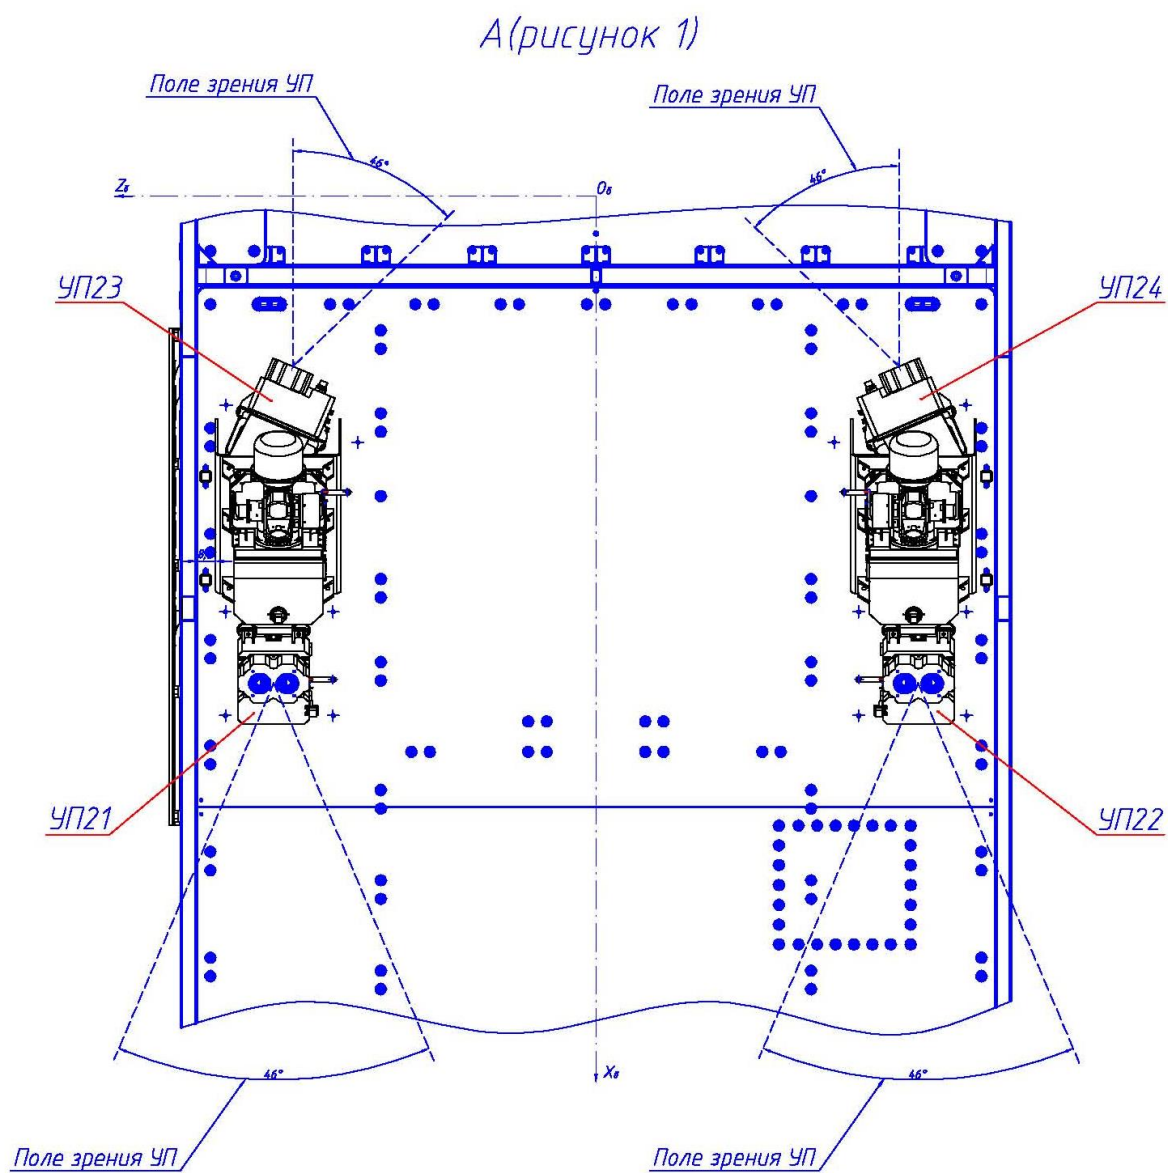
Размещение УП на корпусе КА (Вид А)
